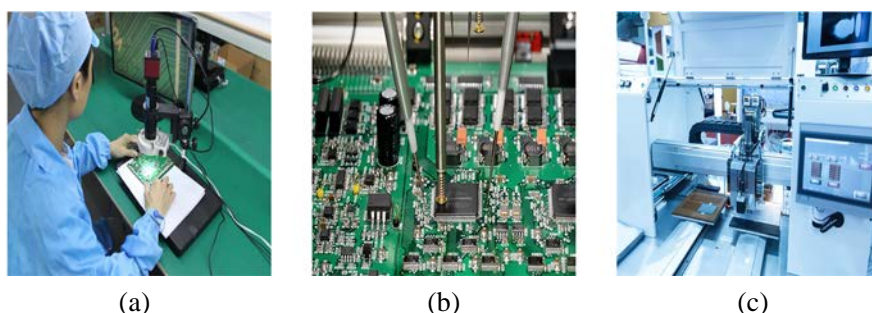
PCB 表面缺陷检测方法：（a）人工目视；（b）电气检测；（c）AOI 检测
